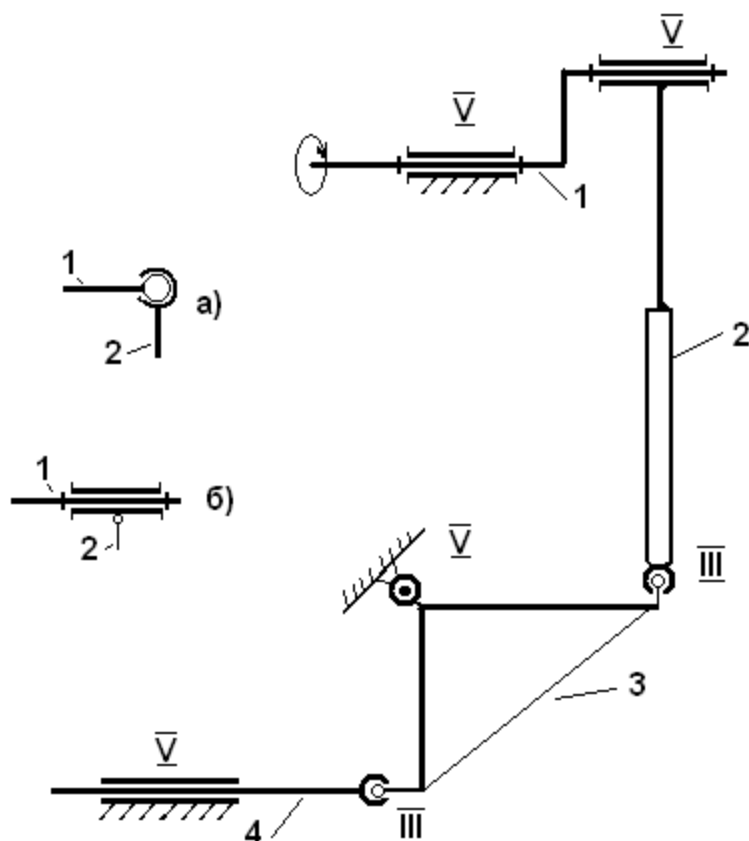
Структурно-кінематична схема механізму привода ріжучого апарата жниварки
